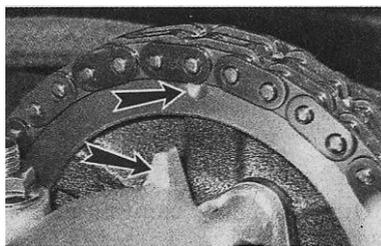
Метки на ведомой звездочке распределительного вала и на постели корпуса подшипников [31]
